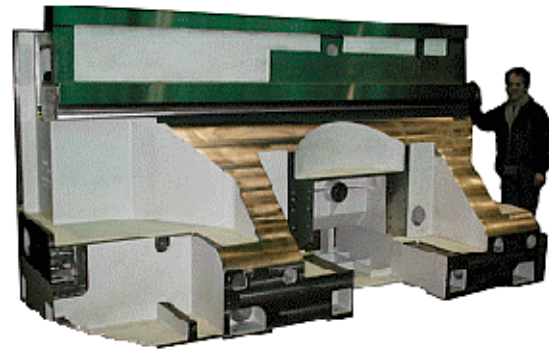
Maschinengehäuse für Vertikaldrehmaschine
